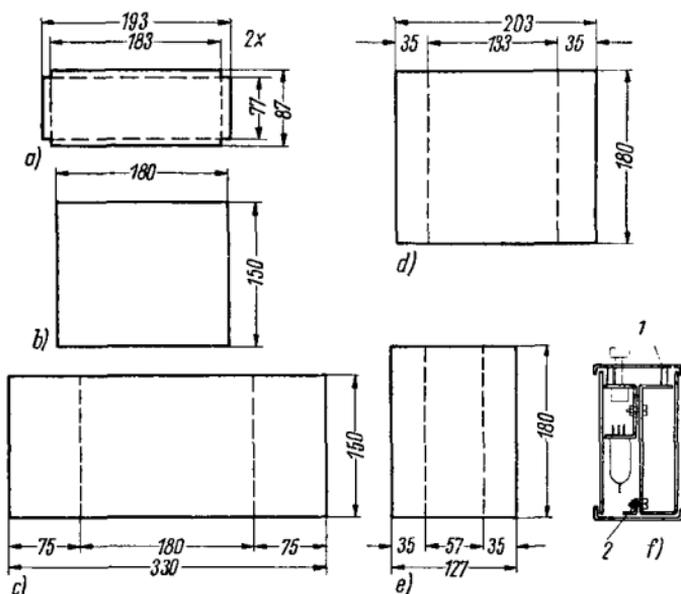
Maßskizze zur Anfertigung des Chassis. Blechmaterial (1 mm dick) für Gehäuse und Chassis.
